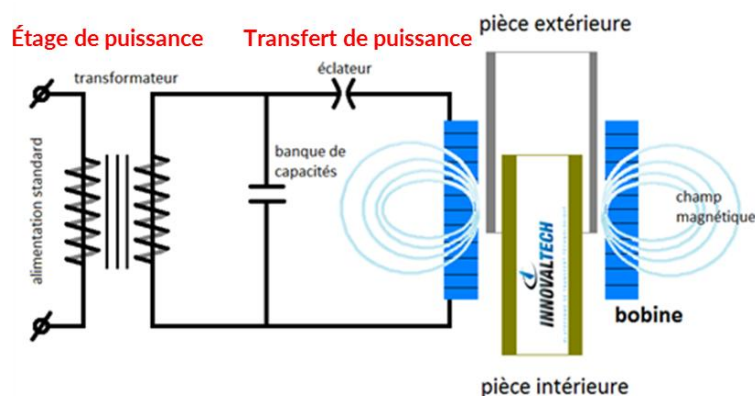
Représentation schématique d'une machine à impulsions magnétiques. Dans cette configuration, la machine est en mode « soudage » de pièces cylindriques.
